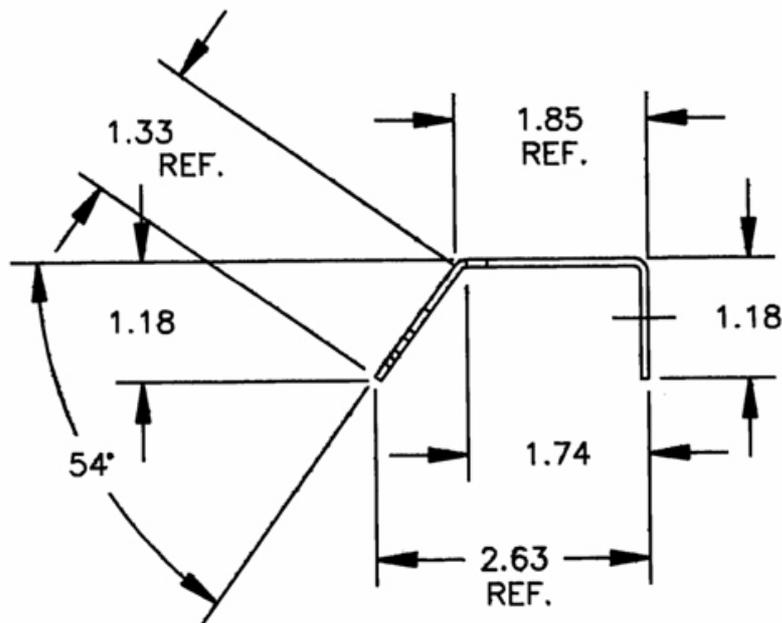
Шина заземления 44В295864-001, размеры, вид сбоку
